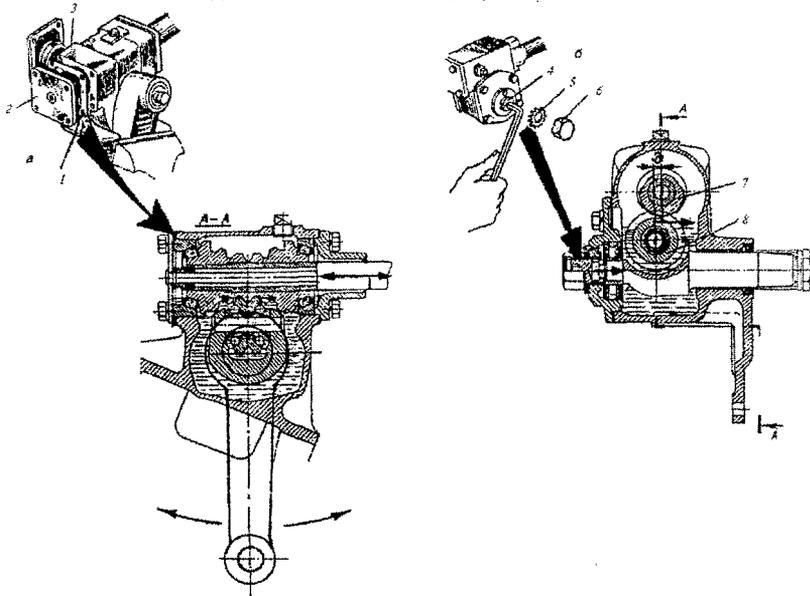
Регулировка рулевого механизма ГАЗ-53А:
